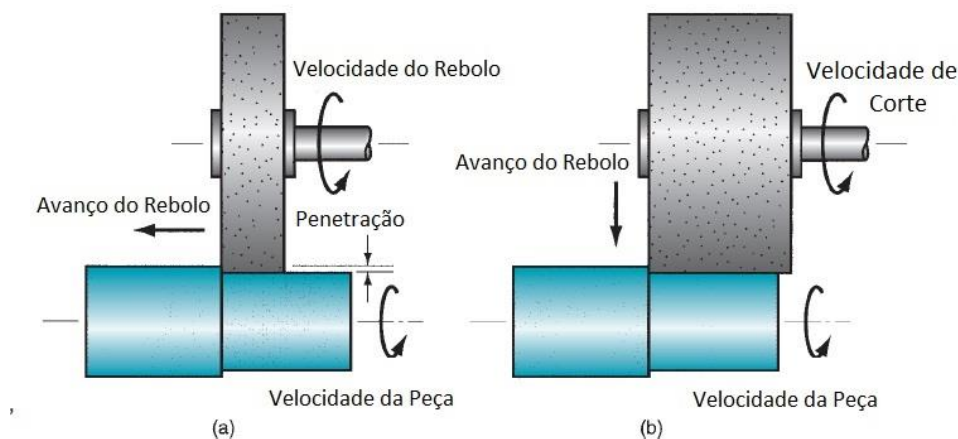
Movimento de avanço da retificação cilíndrica, adaptado de (GROOVE, 2014)
